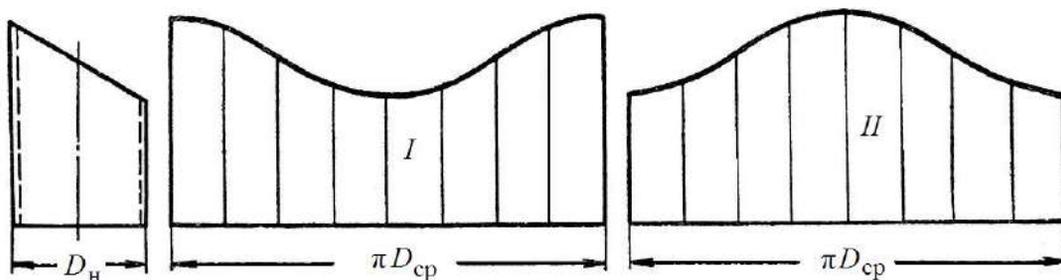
Раскрой заготовки усеченного цилиндра:
